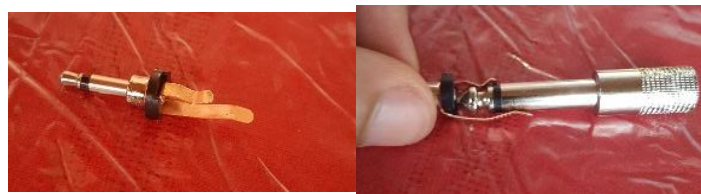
Adaptador de 1/8 a 1/4 desmontado
